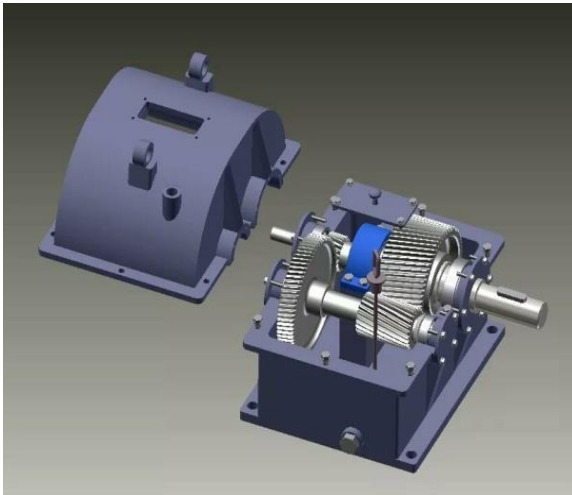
Двухступенчатый горизонтальный соосный редуктор
